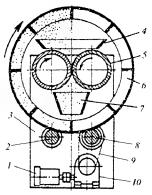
Вальновый смеситель: 1— электродвинатель: 2 гролик; 3 — станина: 4— приемная воронка; 5 — вальны; 6 — кольцевои польемник; 7 гроронка; 8 ролик; 9 цепная передача; 10 гредуктор
